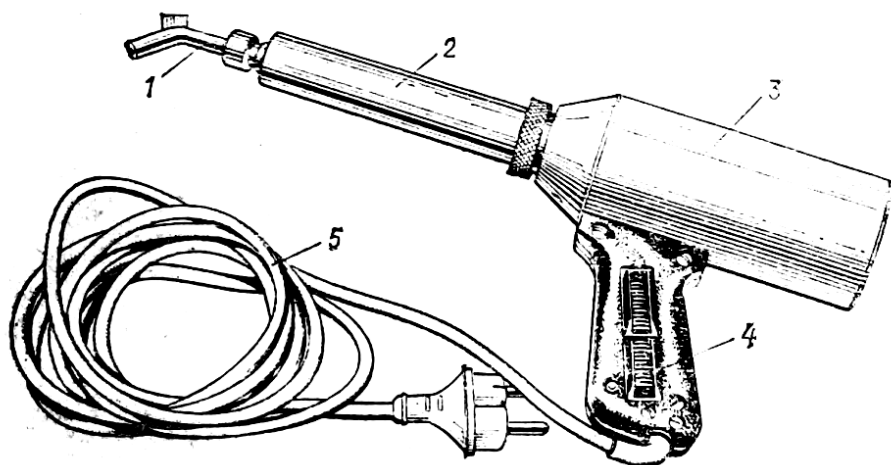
Горелка со встроенным малогабаритным компрессором:
